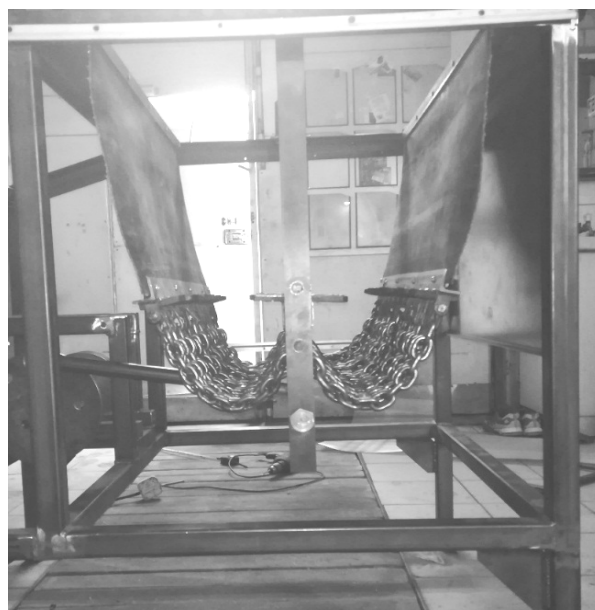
Цепной агрегат с двухволновой рабочей камерой и верхним подвесом маятниковых рычагов (вид сбоку)
